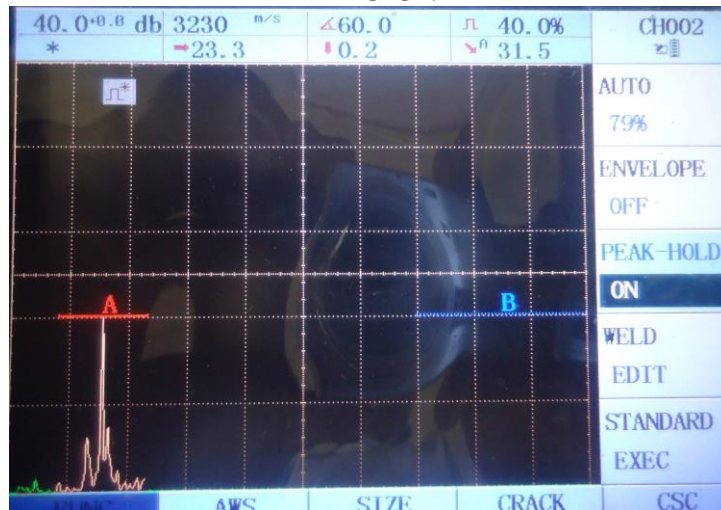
FOTOS DE MEDICIÓN POR ULTRASONIDO EN JUNTAS SOLDADAS DE TANQUES DE ALMACENAMIENTO		F1
